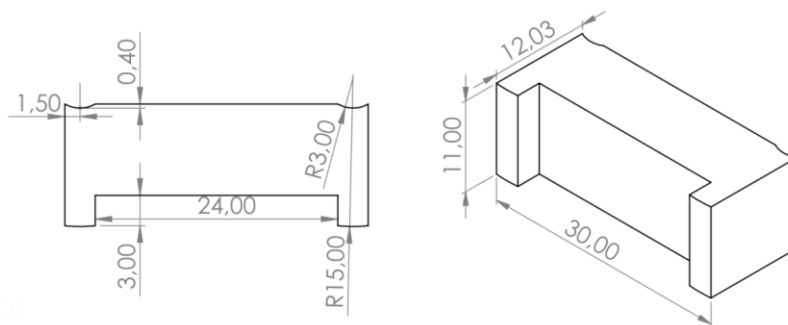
Ponte de contacto cilíndrico (dimensões em mm).
